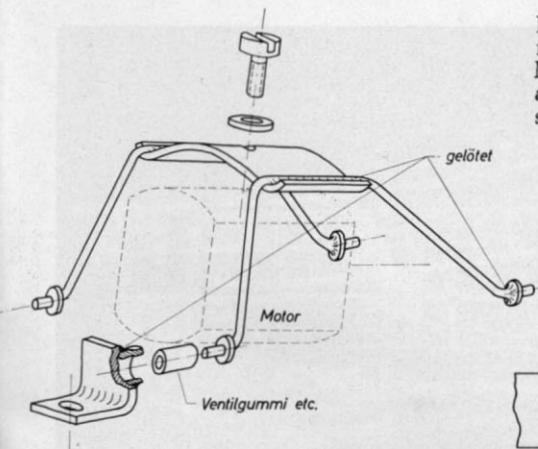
Die Stelzenhalterung für den Motor im Trix-VT 75.
